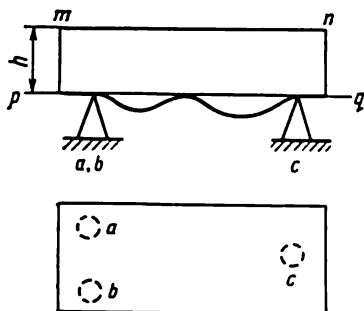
Mise en place d'une ébauche sur des cales ponctuelles
